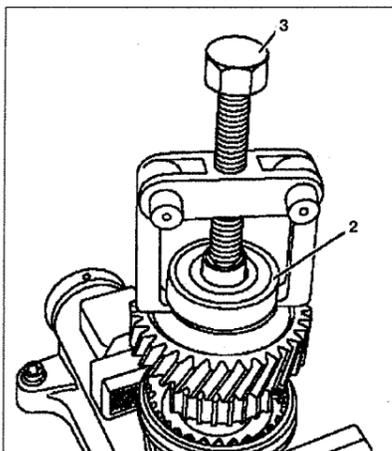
Снятие роликового подшипника (автомобили с двигателями 611.980):
